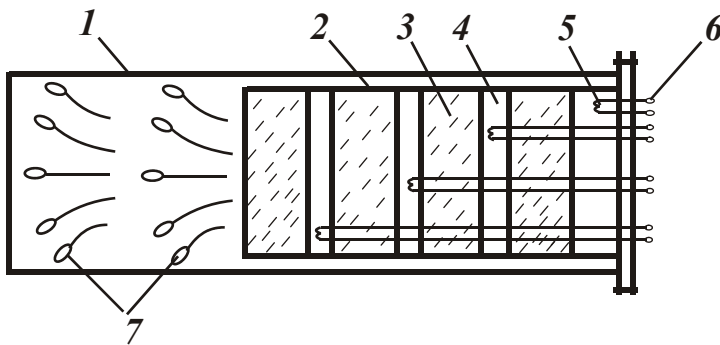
Абразивно-шлифовальная обработка цилиндров с помощью многозарядных патронов: 1 – обрабатываемый цилиндр; 2 – патрон; 3 – абразивный материал; 4 – пороховой заряд; 5 – спираль для зажигания порохового заряда; 6 – клеммы для подачи электрического тока на спираль; 7 – абразивный материал в работе.
